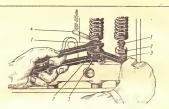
Регулировка зазора с нижним расположением клапанов; 1 — регулировочный винт; 2 — контргайка; 3 — толкатель; 4 — щуп,
